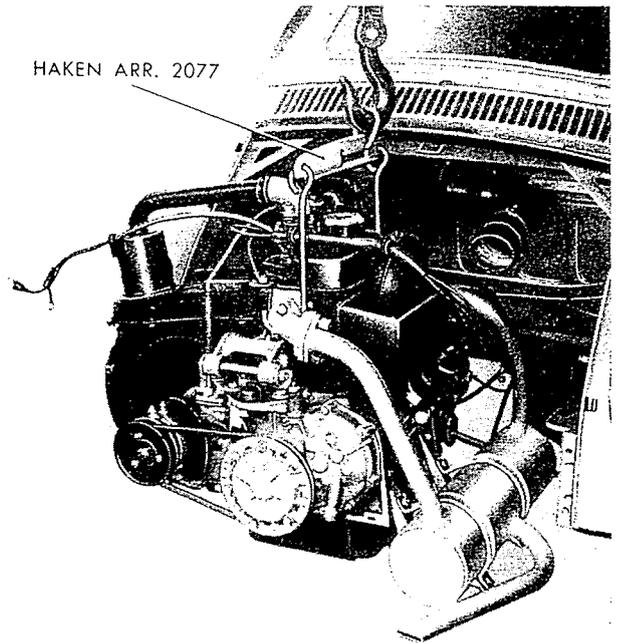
Herausheben des Motors mittels einer Laufkatze mit Haken Arr. 2077.
